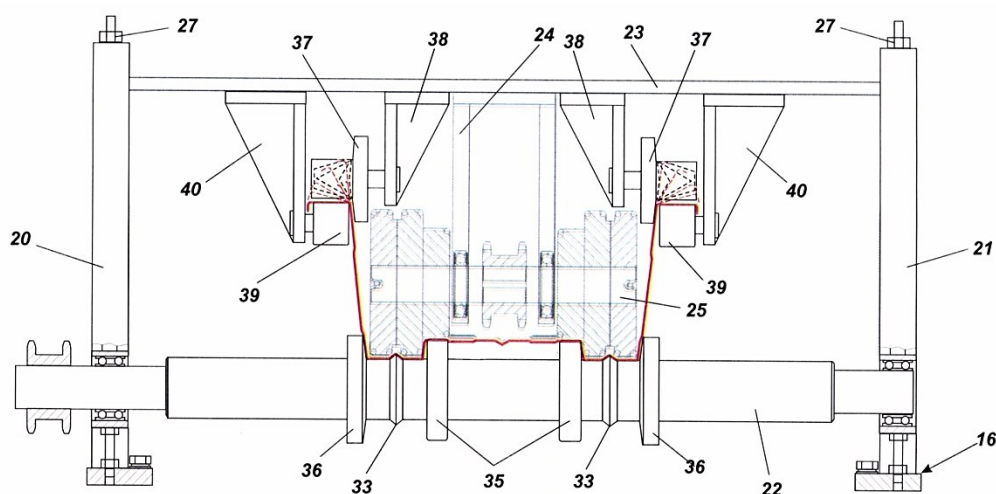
Фрагмент многоклетьевого профилегибочного стана изготовления профиля [5]:
